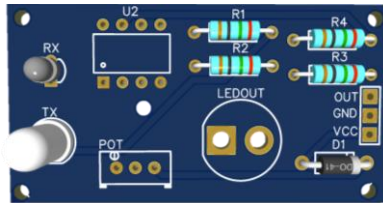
Vista 2D superior del diseño PCB del módulo LEDs.
